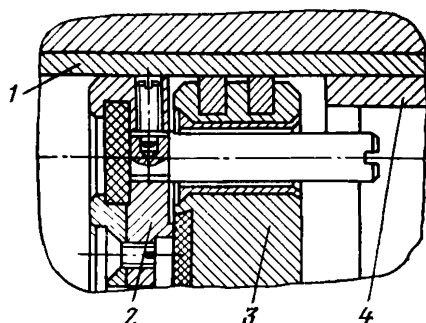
Дутьевой клапан с поршнем и шайбой:
